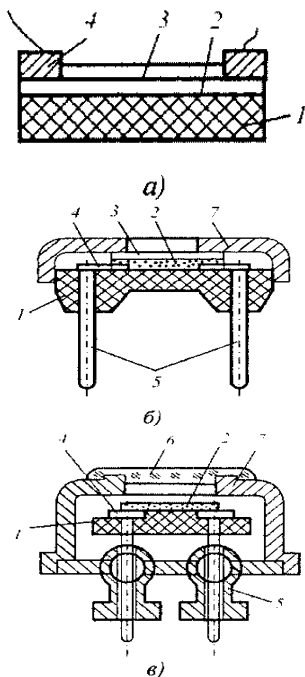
Конструкція фоторезисторів: а) безкорпусні; б) в пластмасовому корпусі; в) в герметизованому корпусі: 1 — ізолююча підкладка; 2 — фоточутливий елемент; 3 — захисний шар лаку; 4 — контакти; 5 — виводи; 6 — скло; 7 — корпус.
